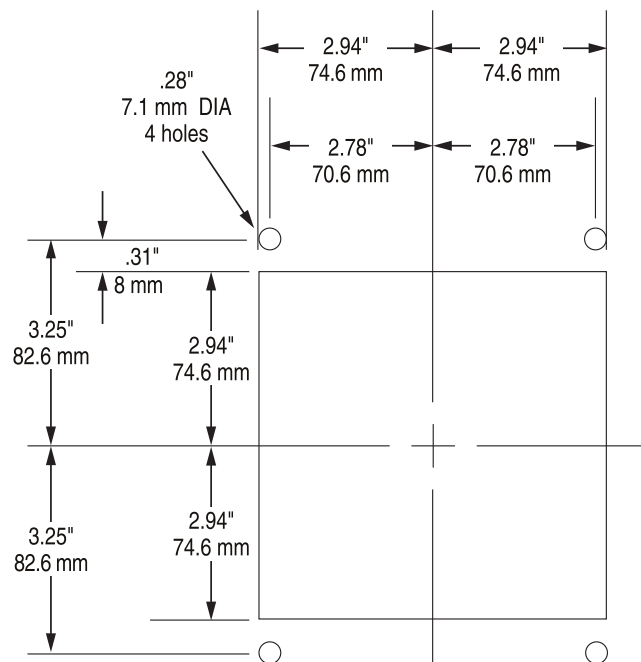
M-0127A & M-0170A Montage Dimensions de découpe
